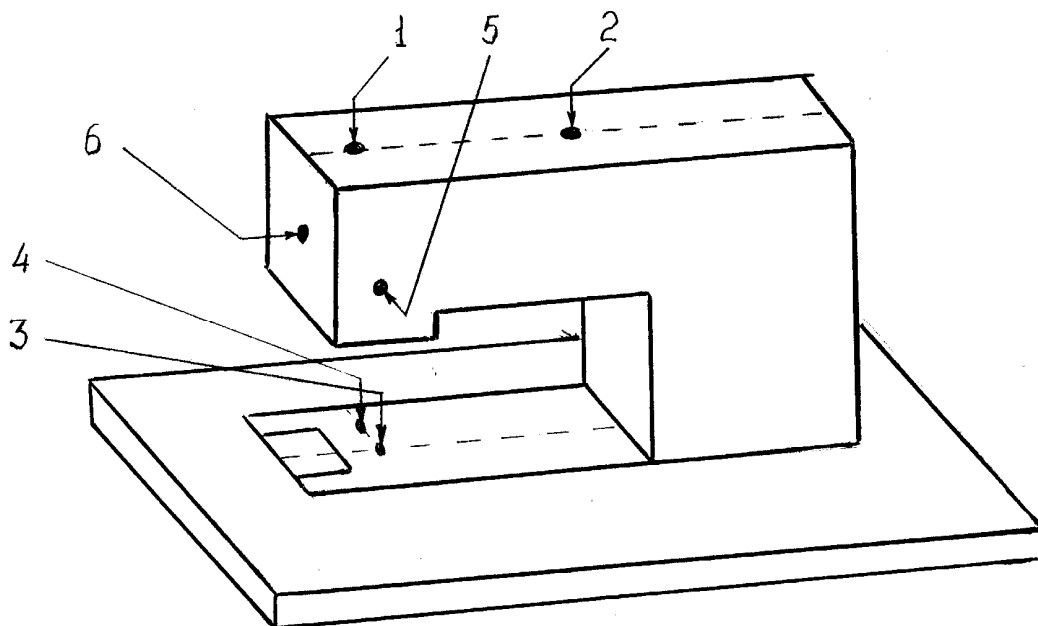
Точки замеров виброскорости корпуса швейной машины
